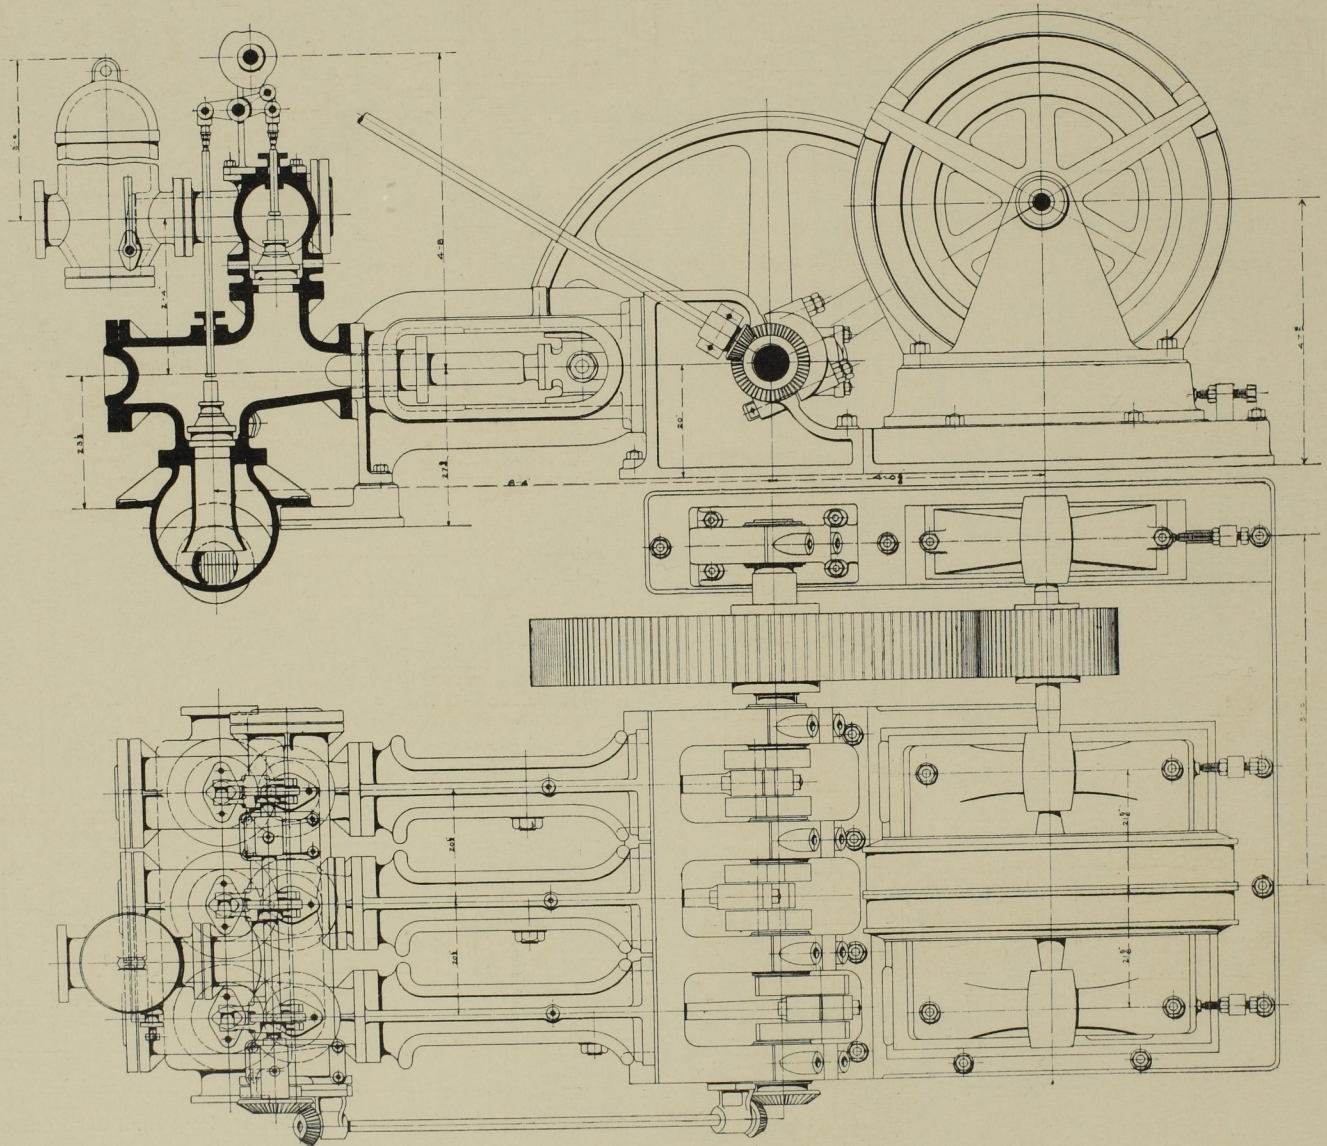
Grundriss und Seitenansicht der Pumpe. Masst. 1 : 32.
